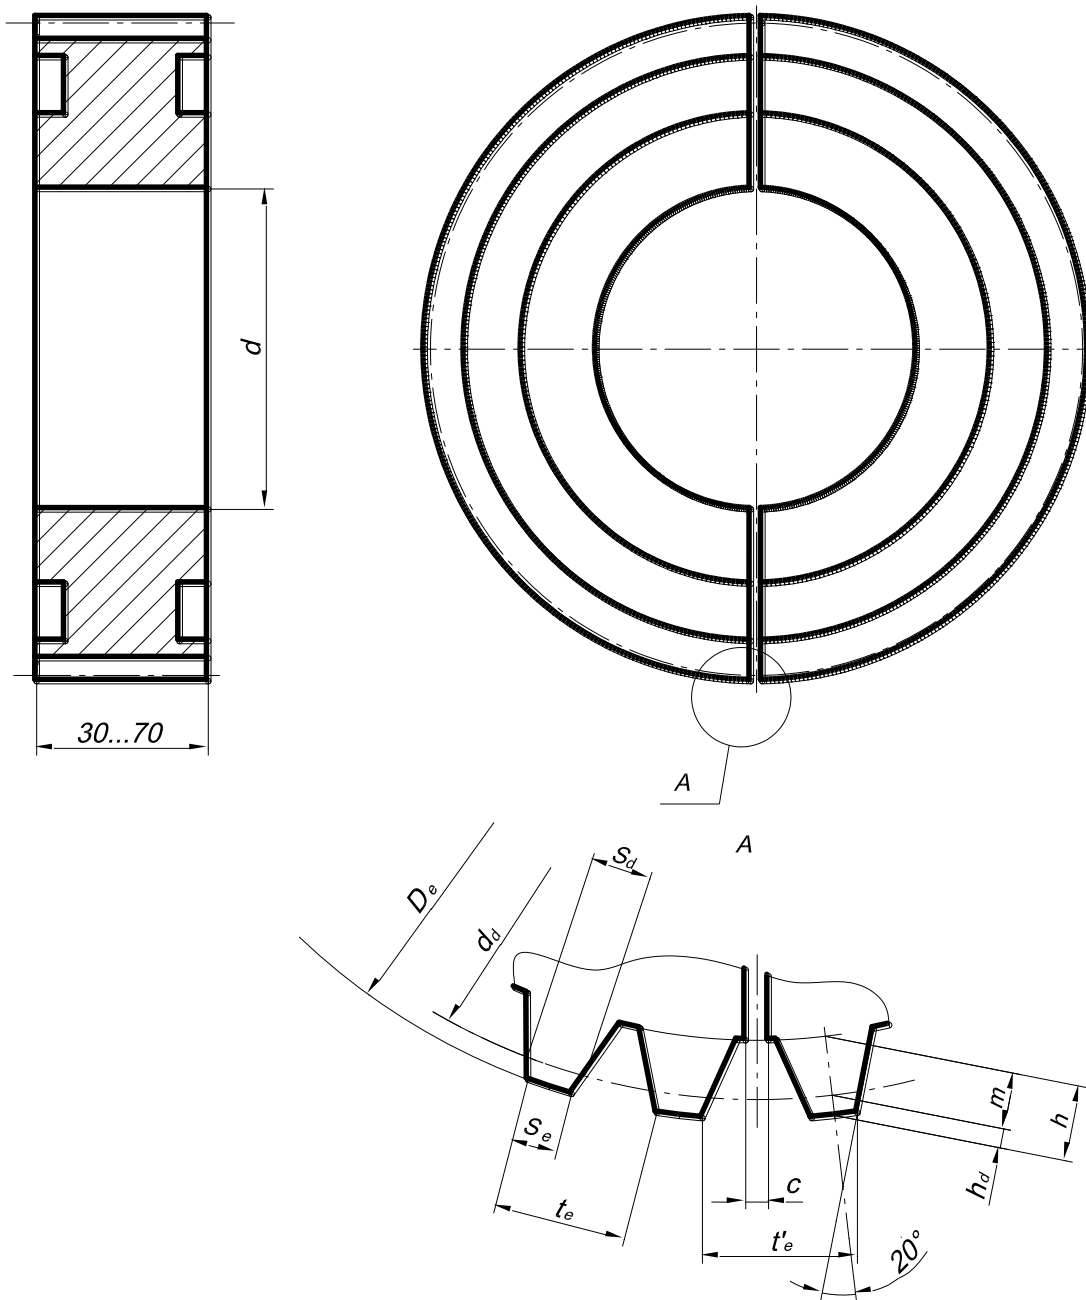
Чертёж рекомендуемой конструкции ротора
